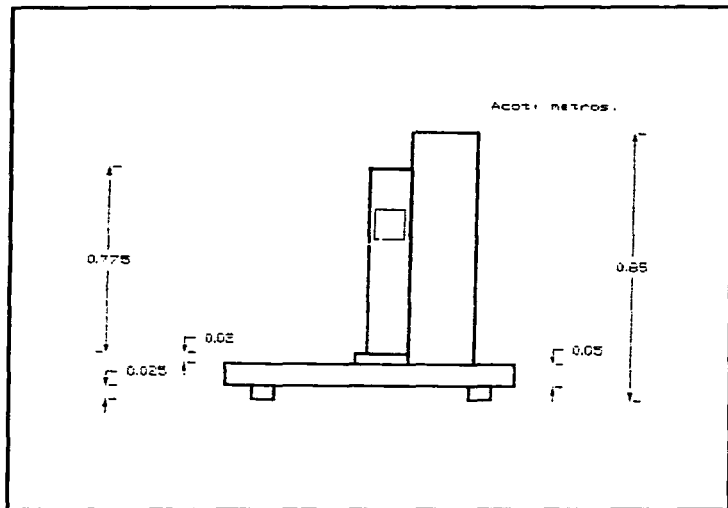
Vista lateral izquierda de la estructura de la estructura del elevador.
